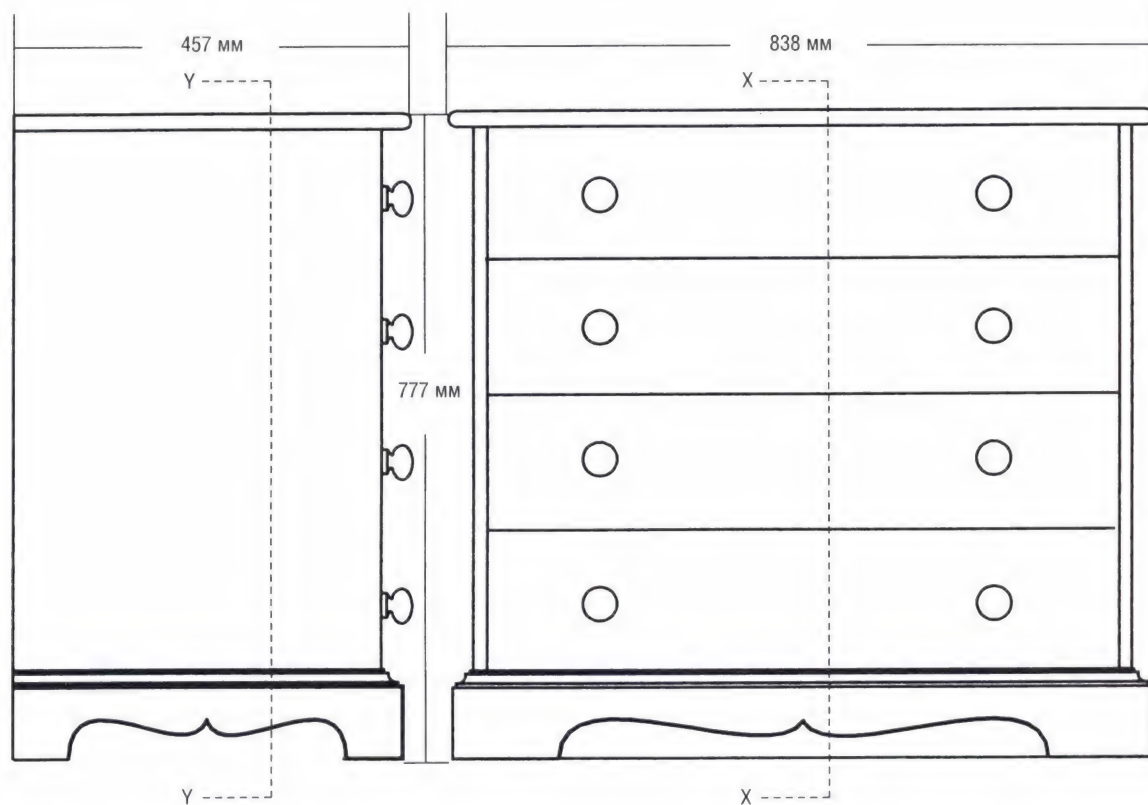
Вид комода спереди и сбоку с размерами.
